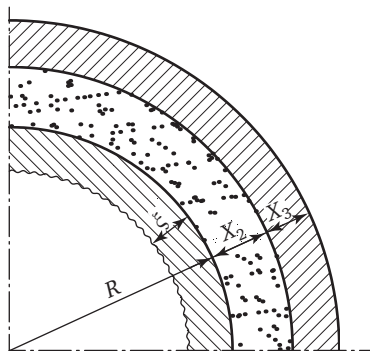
Схема затвердевания цилиндрической или шаровой отливки в металлооболочковой форме
